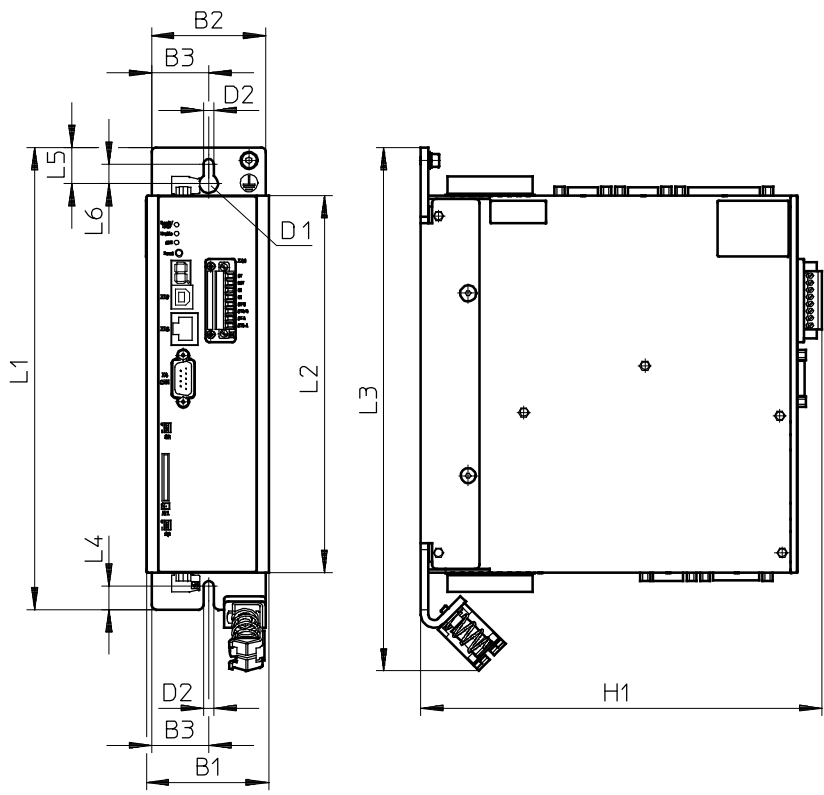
Motorcontroller CMMP-AS-...-M0: Montageplatte
